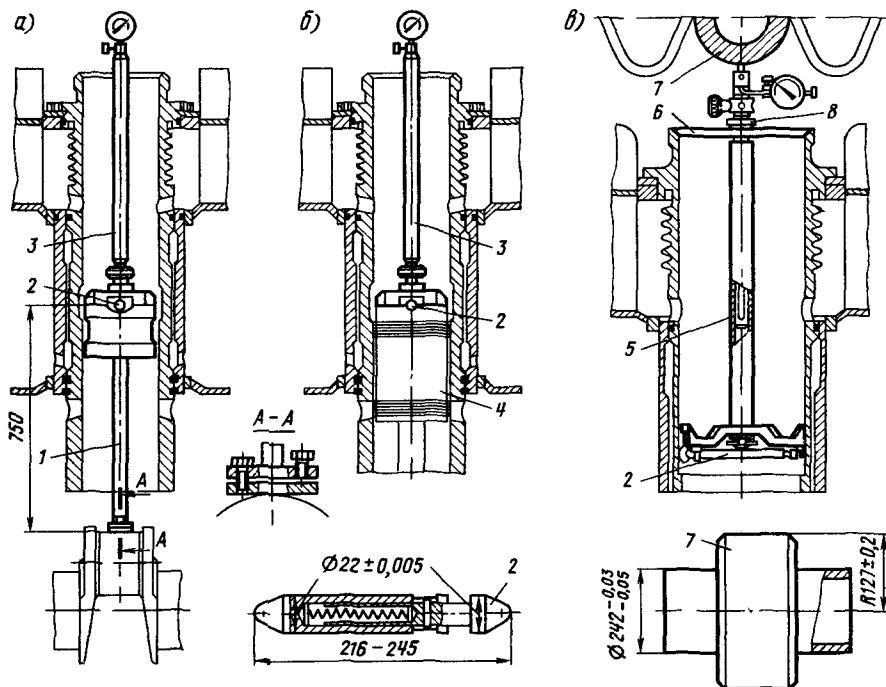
Приспособление для определения длины поршня с шатуном (размером 1,4 и 4,4) дизеля типа Д100
